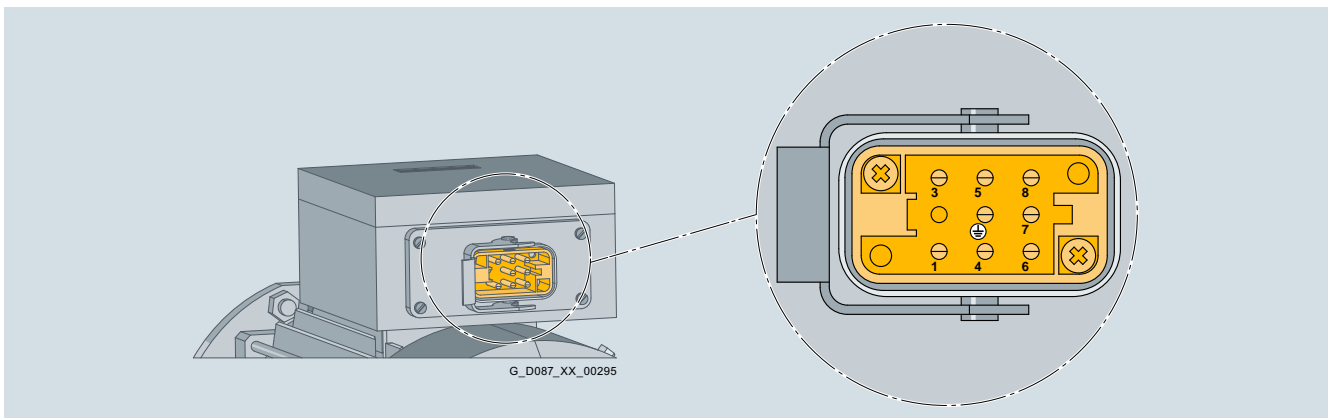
/24 Motorstecker HAN Q8 mit Pinbelegung bei Motorbaugröße 80 bis 132
